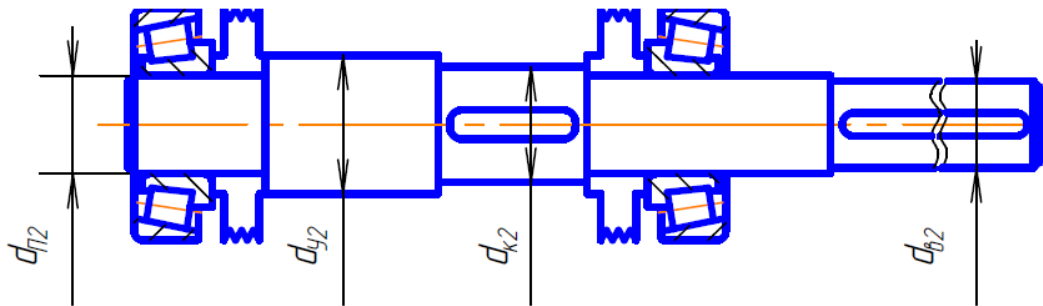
Типова конструкція тихохідного валу кінцевого редуктора
